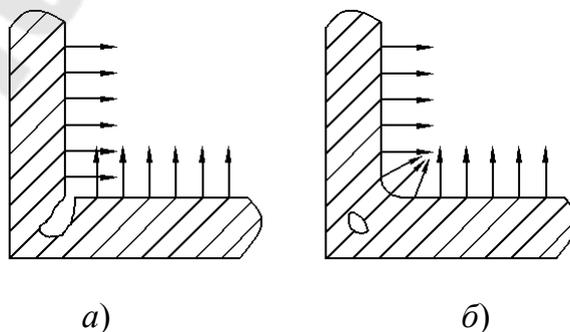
Схема образования зон перегрева и образования усадочно-газовой раковины при разных вариантах сопряжения стенок отливки
